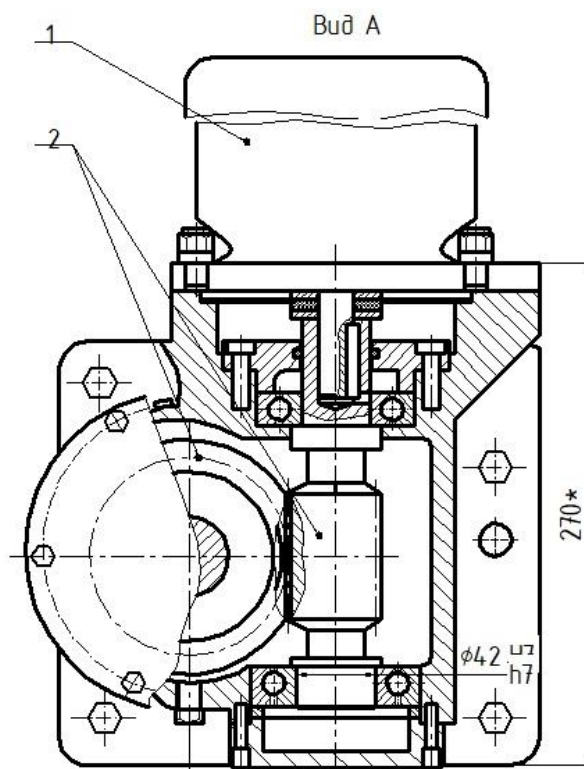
Механизм регулирования закрытой высоты прессы
